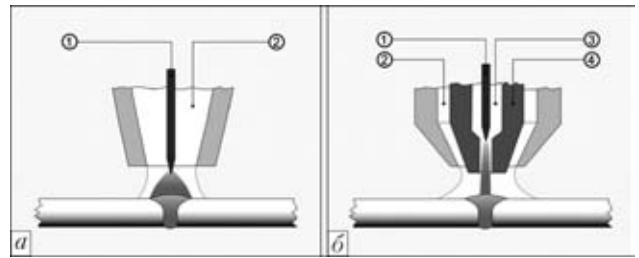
При сравнении со сваркой ТИГ (а) плазменная сварка (б) открывает новые возможности применения и дает многочисленные преимущества: 1 — вольфрамовый электрод; 2, 3 — защитный и плазменный газ; 4 — сопло для плазмы
